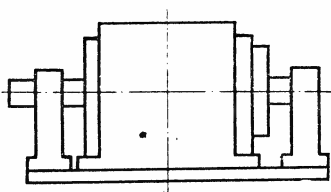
Схематический чертеж машины со стойковыми подшипниками
